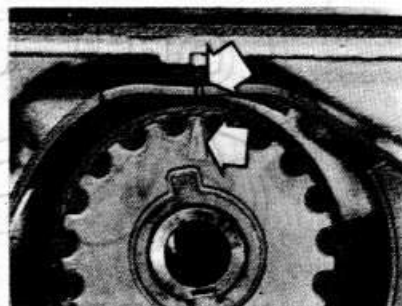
Стрелка на звездочке коленвала совпадает с риской на задней крышке (указано стрелками) при положении поршня N 1 в ВМТ — двигатель 1,6 л
